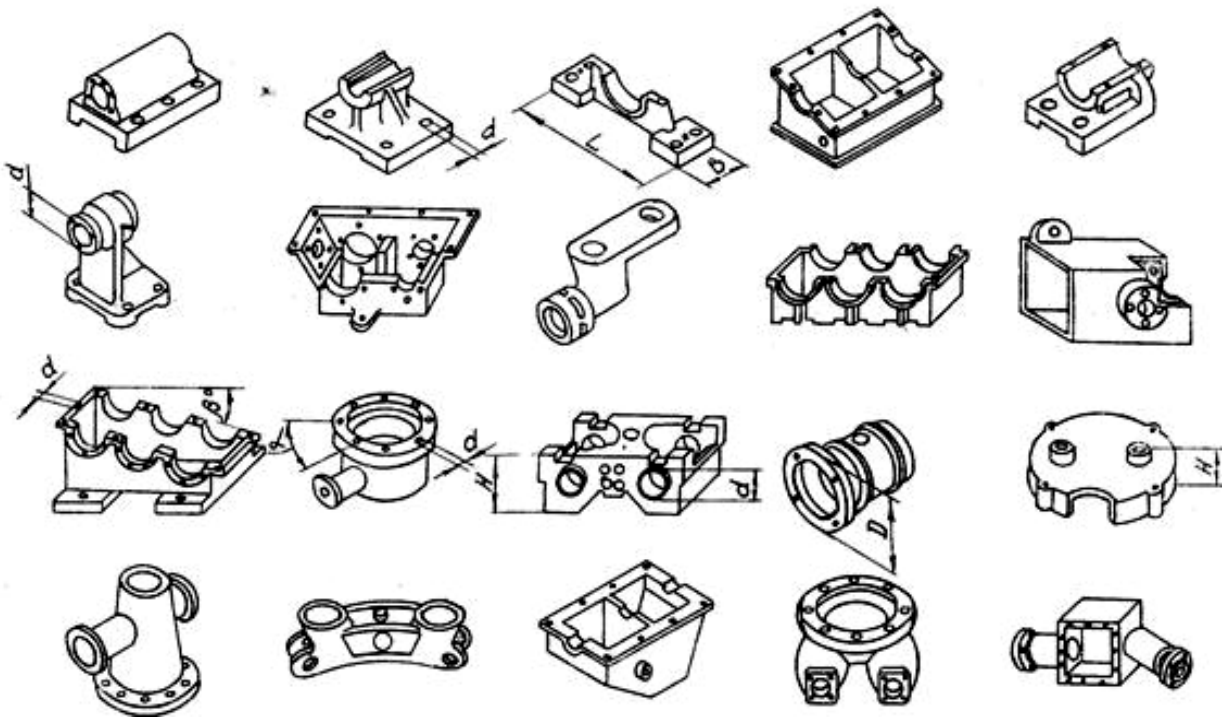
Фрагмент бібліотеки типових деталей для кодування (корпусні деталі)
